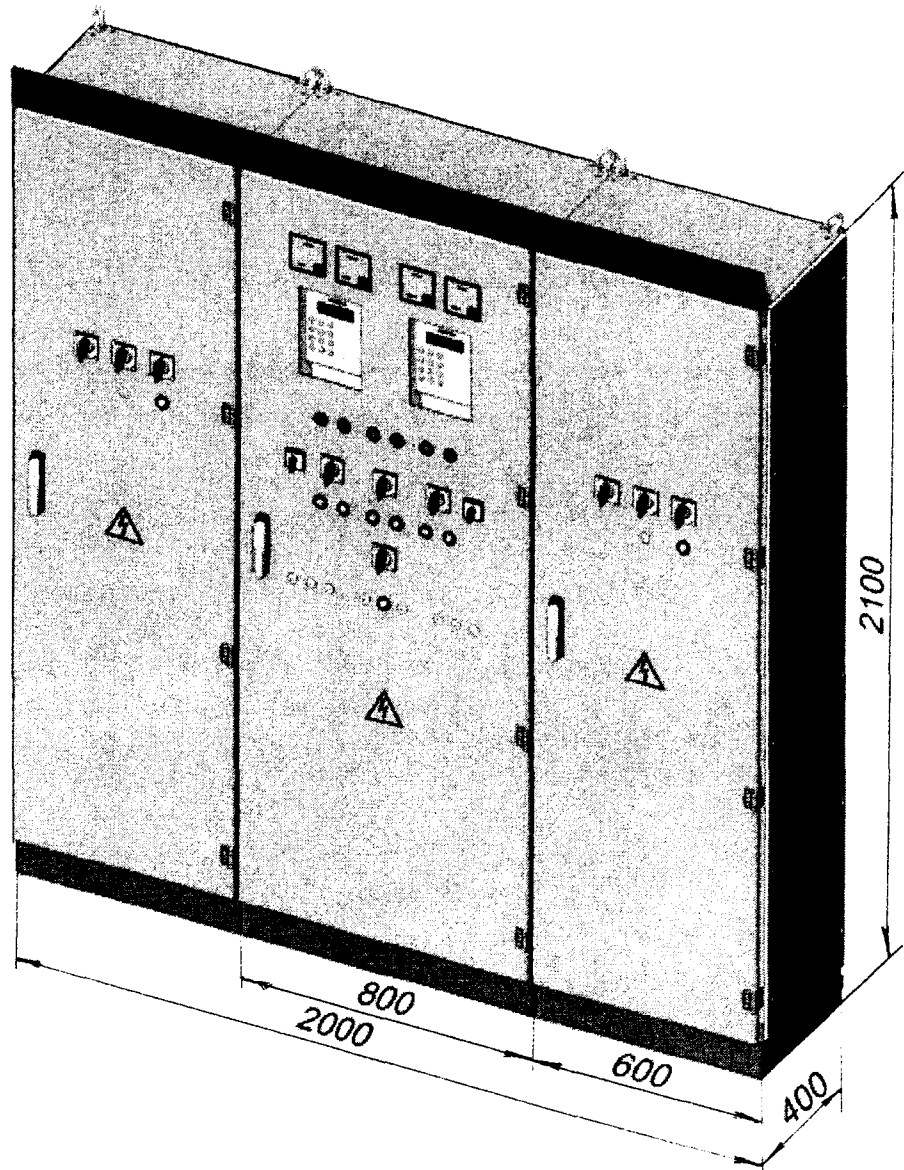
Внешний вид и габаритные размеры щита ЩСН-11-08-21УХЛ4 (ПСН-1114.1; ПСН-1101; ПСН-1114.1)
